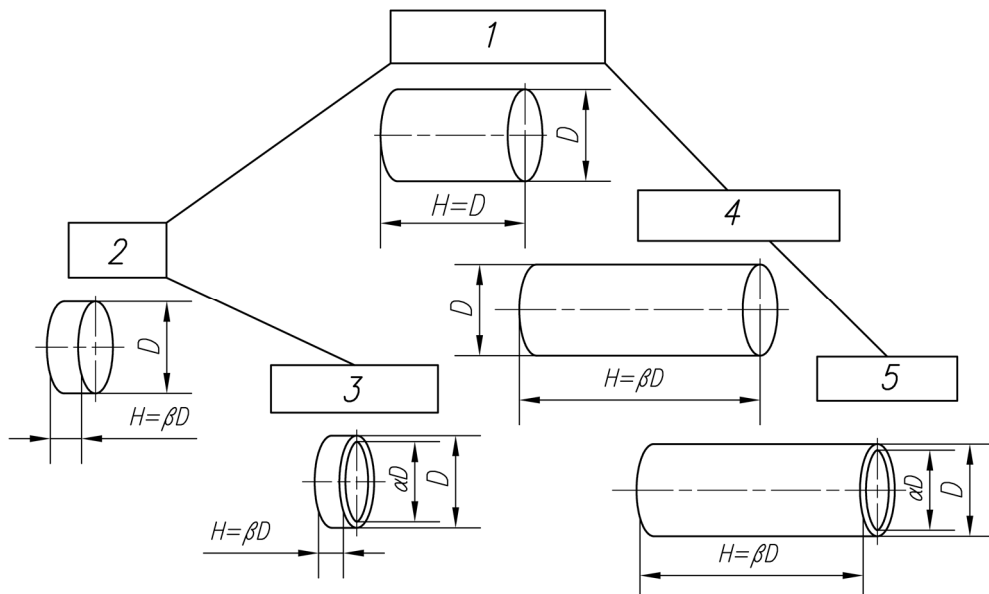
Детали типа тел вращения: 1 – цилиндр; 2 – диск; 3 – кольцо; 4 – стержень; 5 – труба
